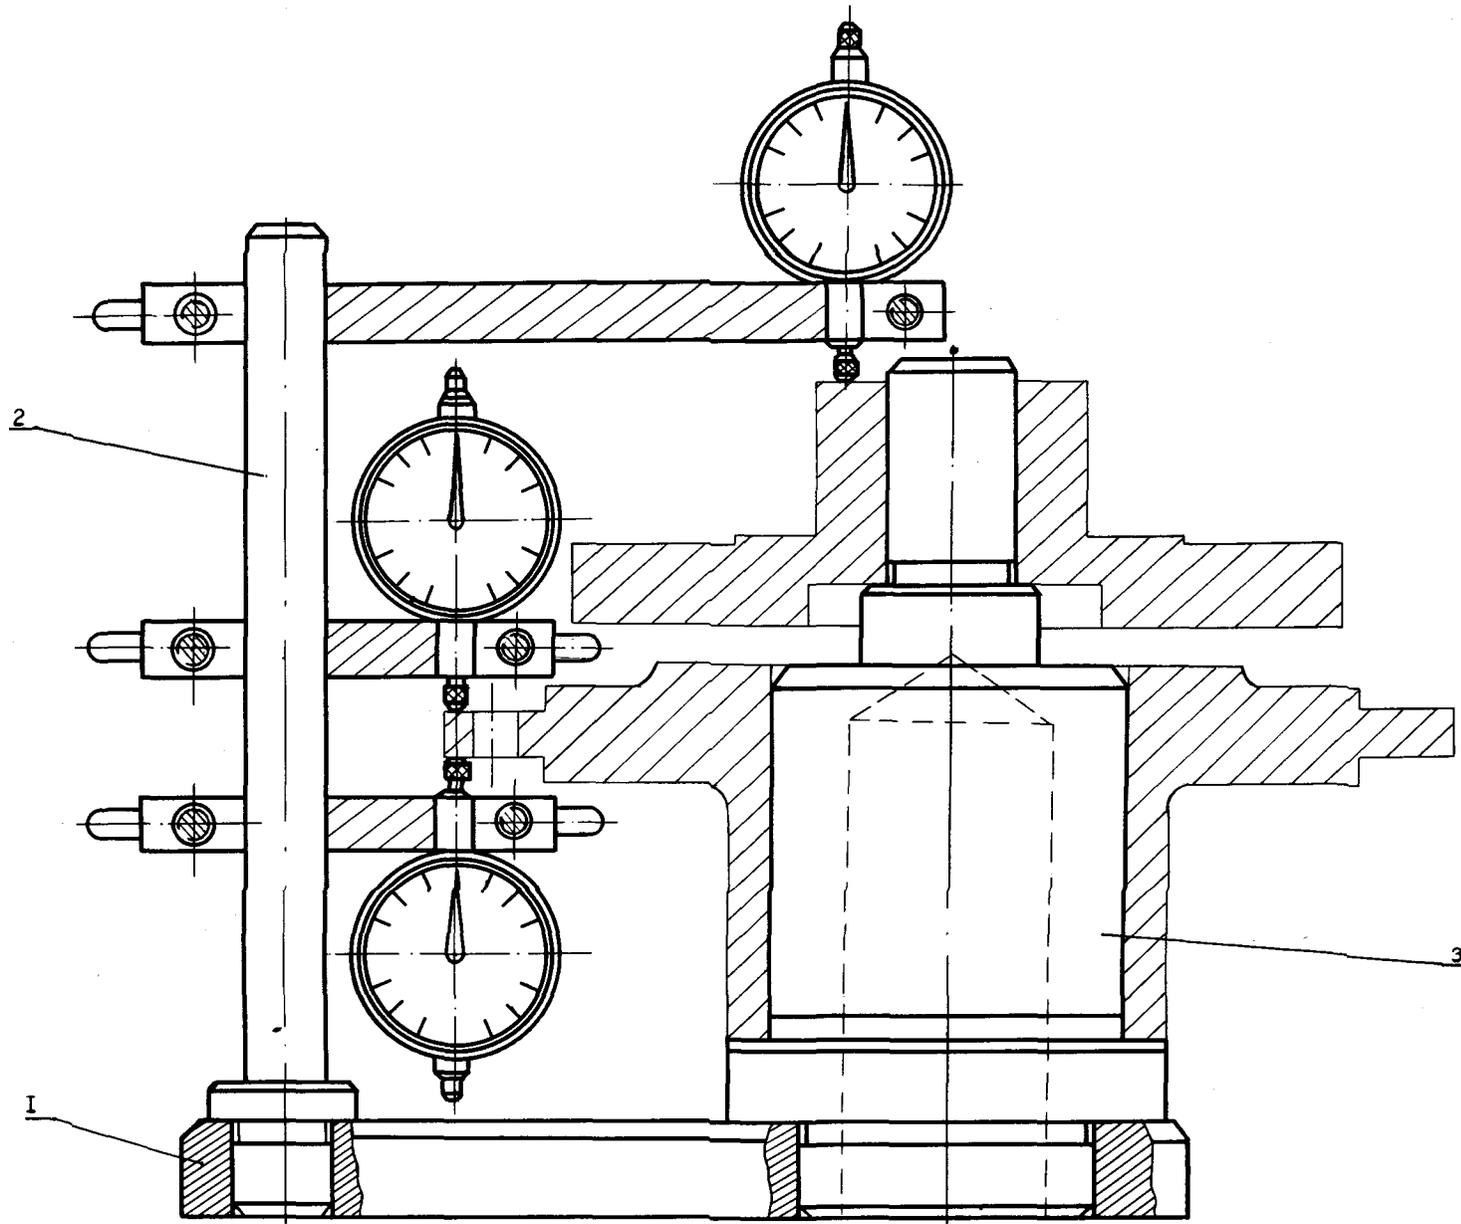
Групповое контрольное приспособление для проверки торцового биения:
